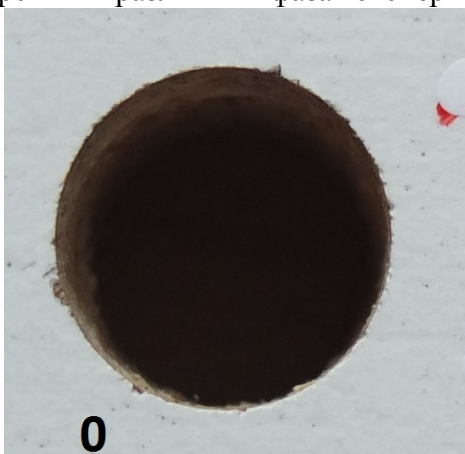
Внешний вид отверстия выполненного фабричным новым сверлом (вид со стороны входа инструмента)
